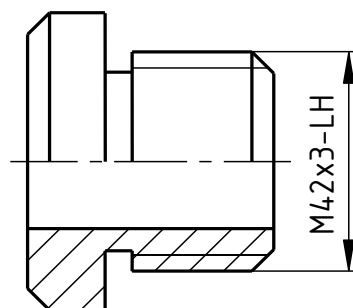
Указание размеров метрической резьбы на чертеже детали
